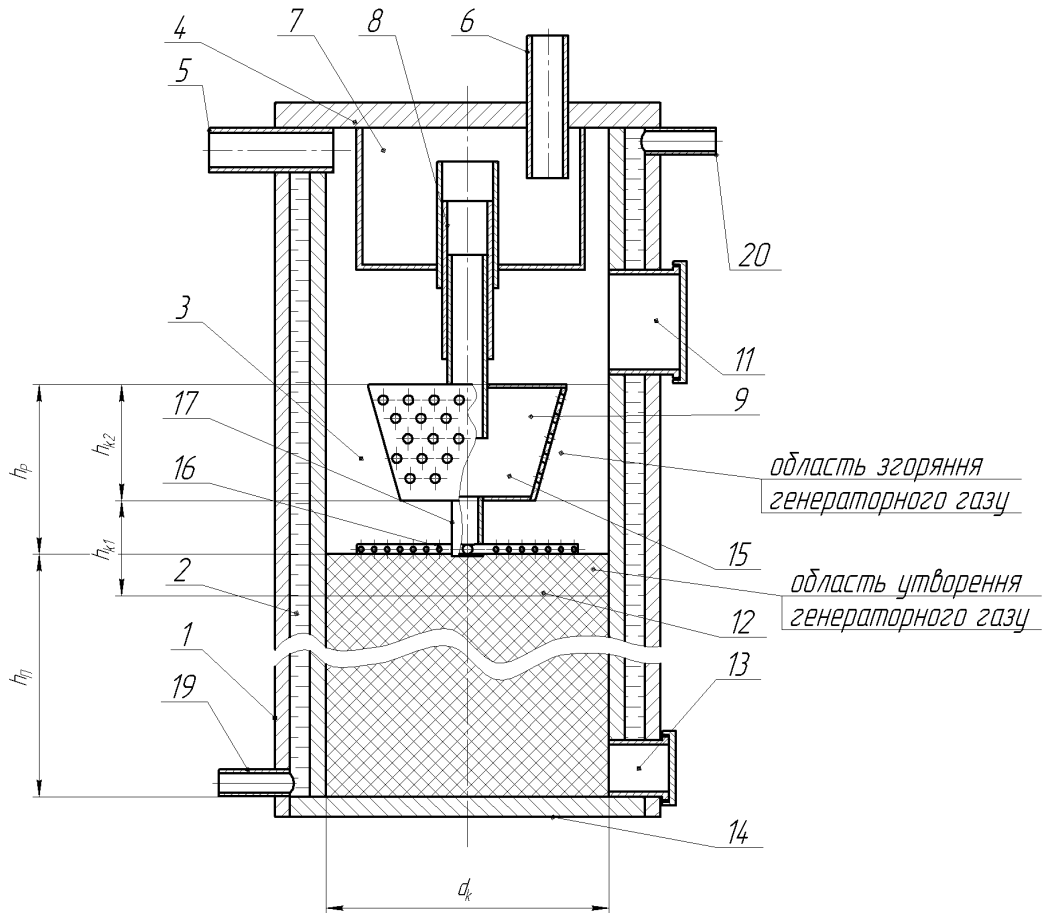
Загальний вигляд котла для спалювання соломи: 1 – корпус; 2 – порожнина; 3 – камера згоряння; 4 – кришка; 5 – патрубок для видалення продуктів згорання; 6 – патрубок для подачі повітря, 7 – проміжна ємкість; 8 – напрямна; 9 - розсіювач повітря; 10 – отвори, 11 – дверцята для палива; 12 – паливо; 13 – дверцята для попелу; 14 – днище; 15 – верхня секція розсіювача повітря; 16 – нижня секція розсіювача повітря; 17 – трубчастий; 18 – трубчасті елементи; 19 – патрубок для подачі холодної води; 20 – патрубок для відведення гарячої води; d_k – діаметр котла; h_n – висота палива; h_p – висота розпилювача повітря; h_{K1} – висота області утворення генераторного газу; h_{K2} – висота області згоряння генераторного газу.
